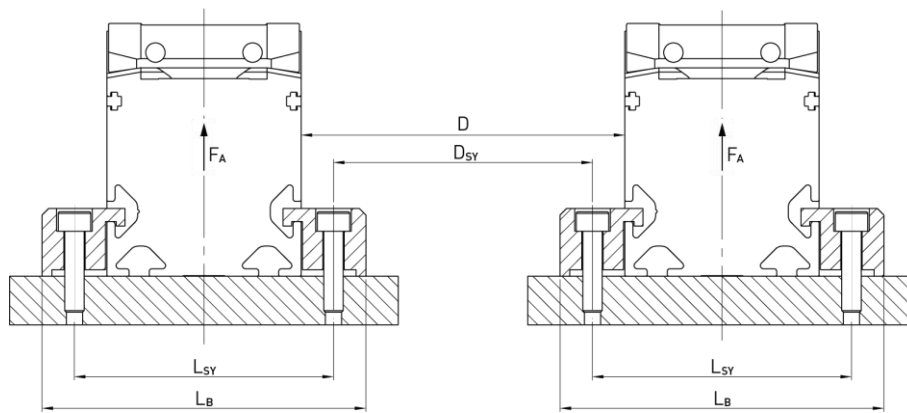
Befestigung mit Spannprofilen – HM040B, HM060B, HM080B
